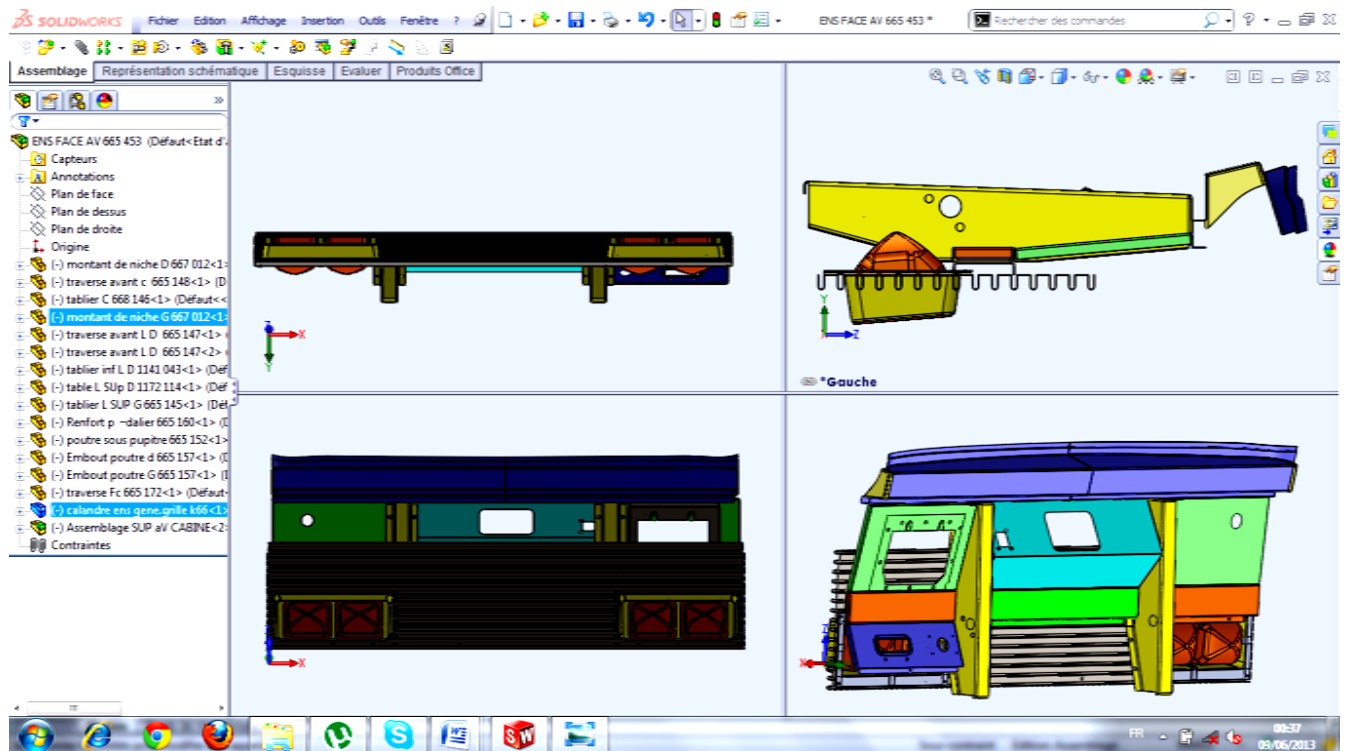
exemple d'ensemble face avant de la cabine du K66
